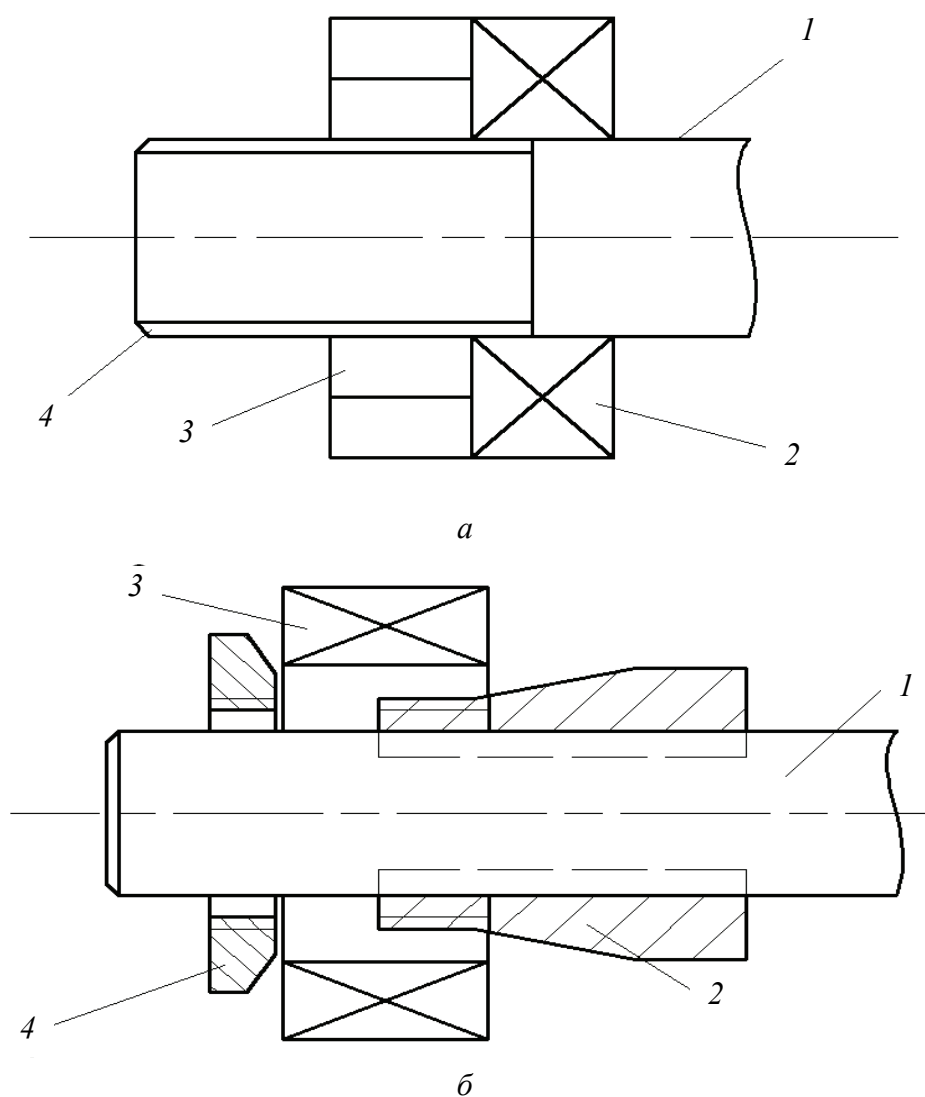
Схемы сборки подшипников качения: *а* – 1 – вал; 2 – подшипник; 3 – гайка; 4 – резьба; *б* – 1 – вал; 2 – втулка разрезка; 3 – подшипник; 4 – гайка
